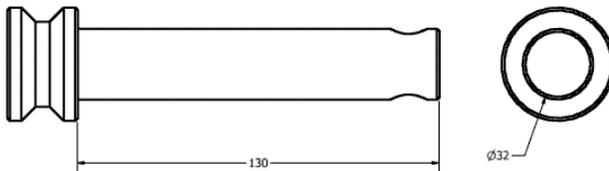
Oberlenkerbolzen komplett Ø32mm.
